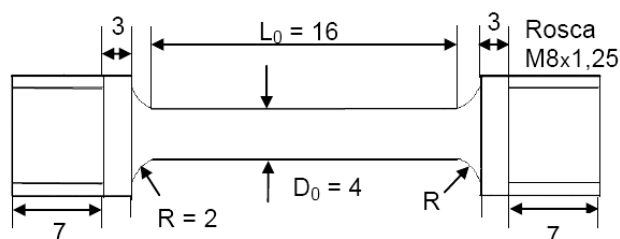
Desenho esquemático de um corpo de prova utilizado nos ensaios mecânicos
